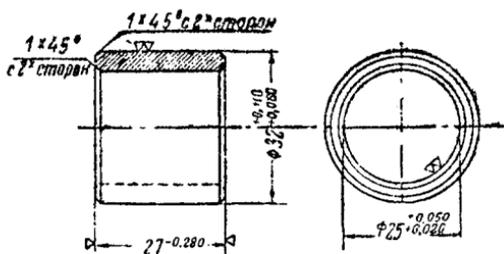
Дет. № 1043. Втулка промежуточной шестерни.
